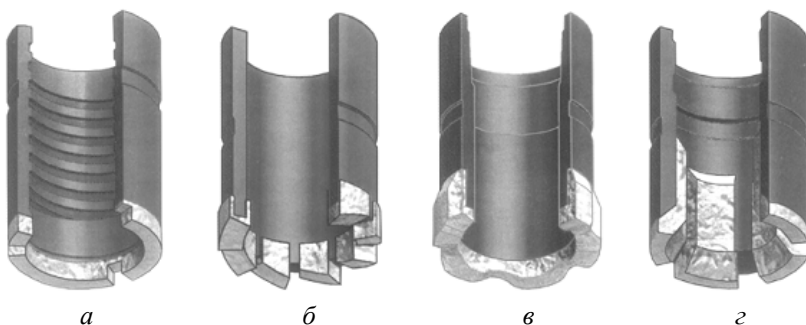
Фрезеры кольцевые: а – типа 11Ф с плоской поверхностью; б – типа 11Ф с зубчатой поверхностью; в – типа 12Ф с волнистой поверхностью; г – типа 13Ф с конической поверхностью
